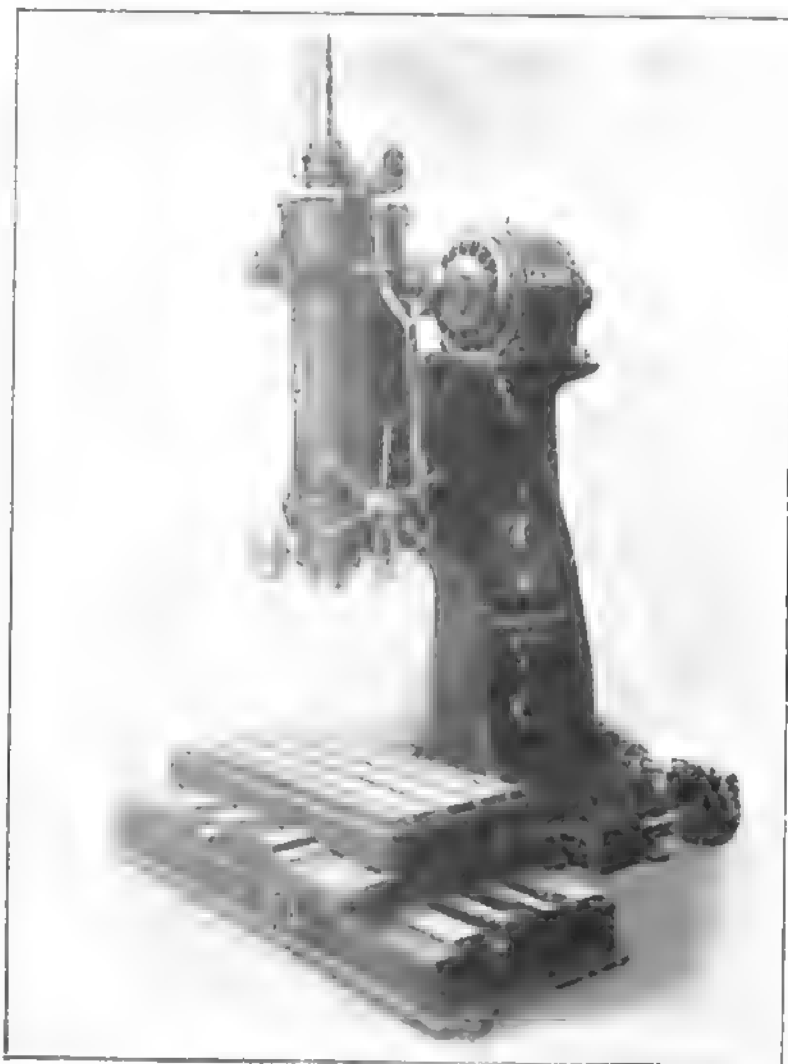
Bohrmaschine mit horizontalem Reguliermotor.
